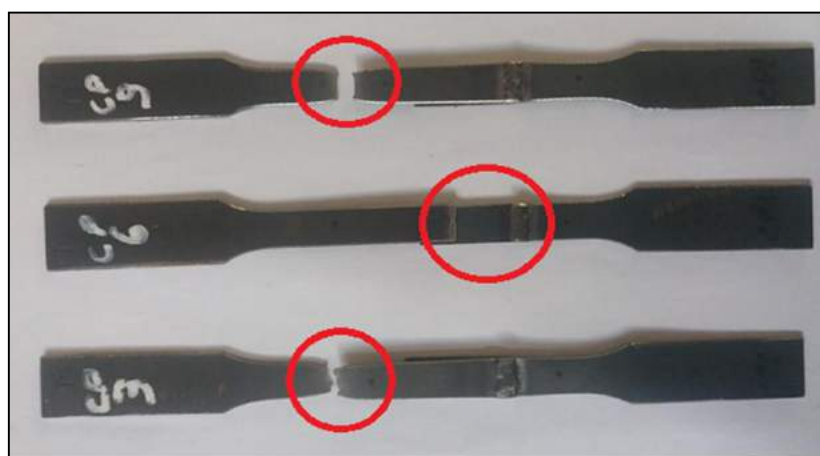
Corpos de prova do material com solda sobreposta com a estrição em destaque
